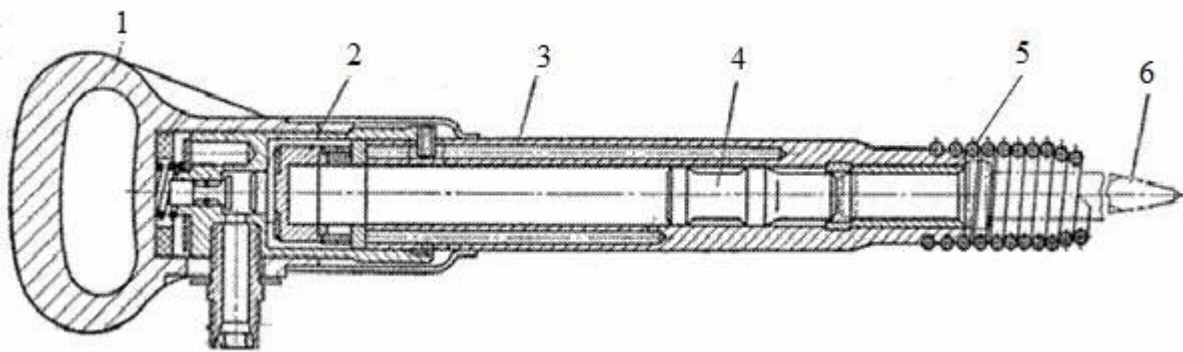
Конструкция ручного пневматического отбойного молотка.
